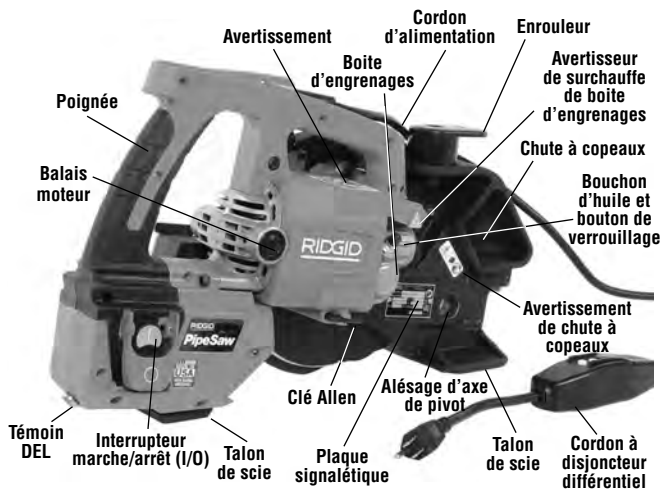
Scie à tubes transportable PCS-500 vue de face
